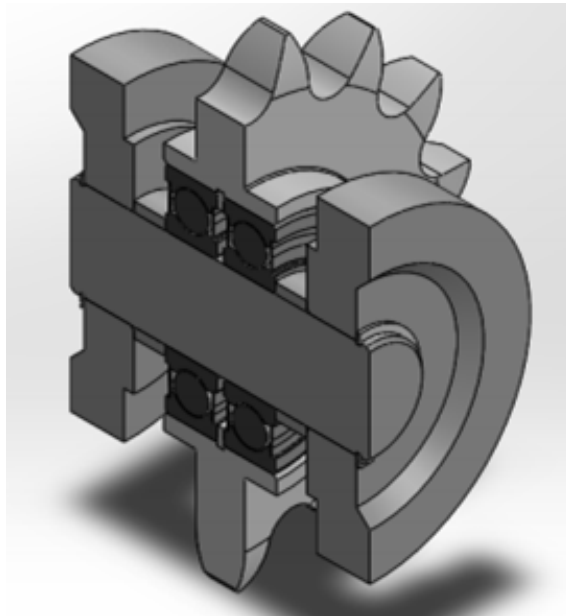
Конструкція опори верхньої зірки ланцюгового приводу
